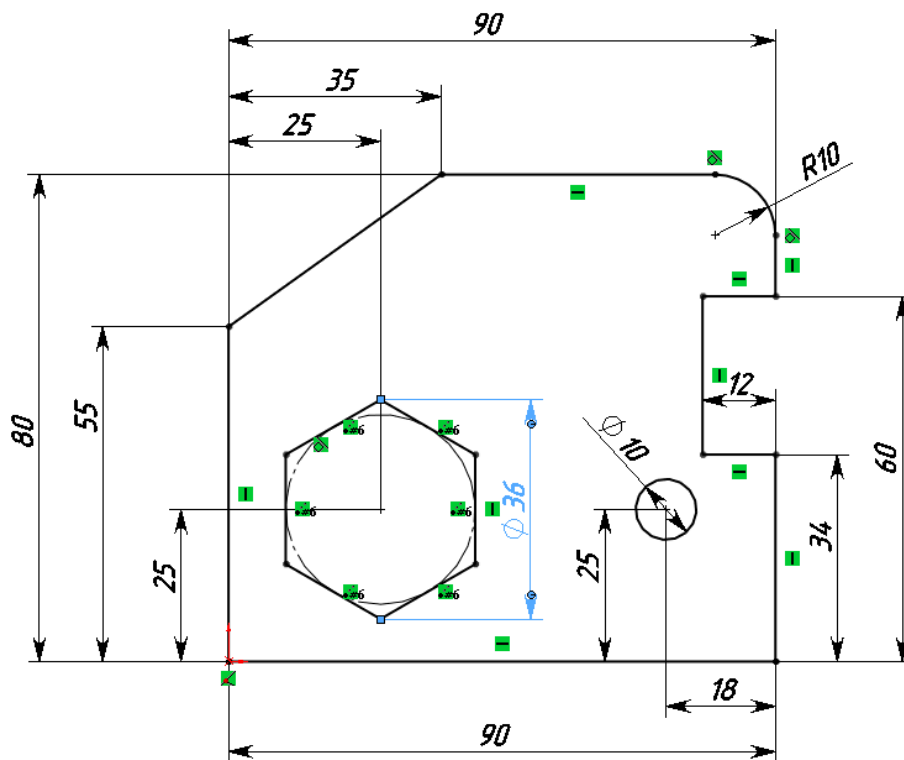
Эскиз элемента детали, выполненный CAD среды SolidWorks
